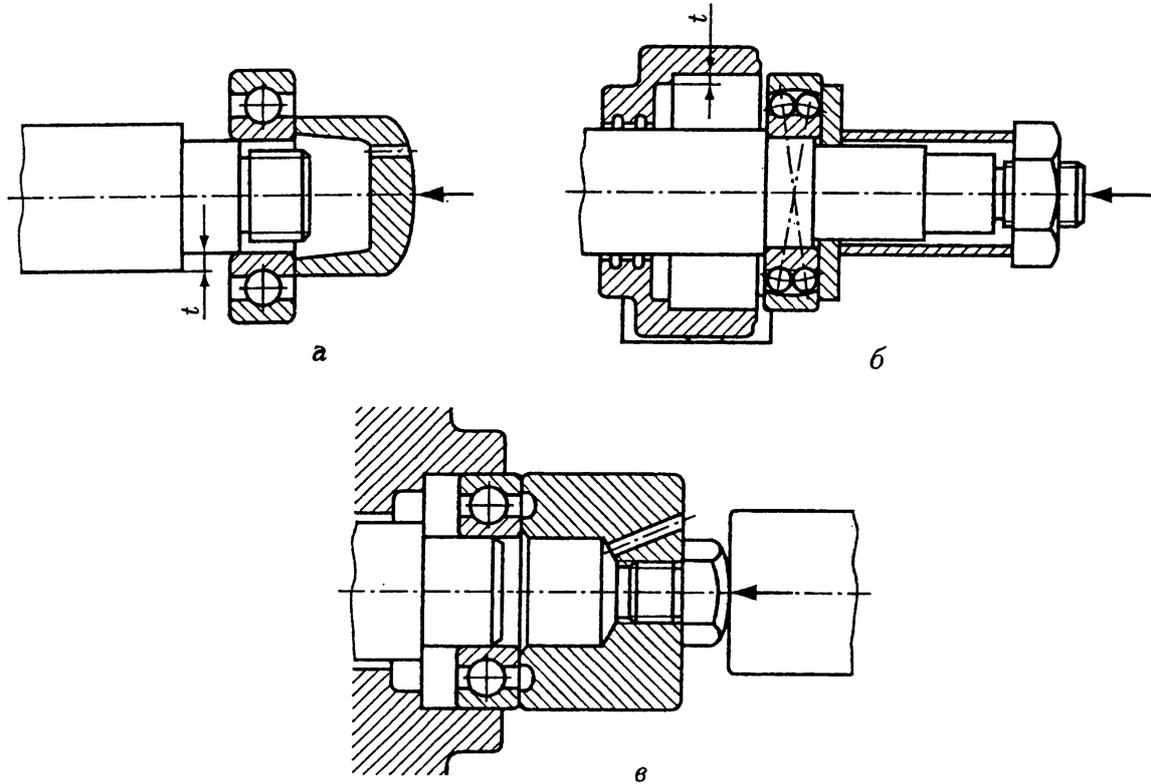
Способы монтажа подшипников на вал (а), в корпус (б) и одновременно на вал и в корпус (в) [5]
